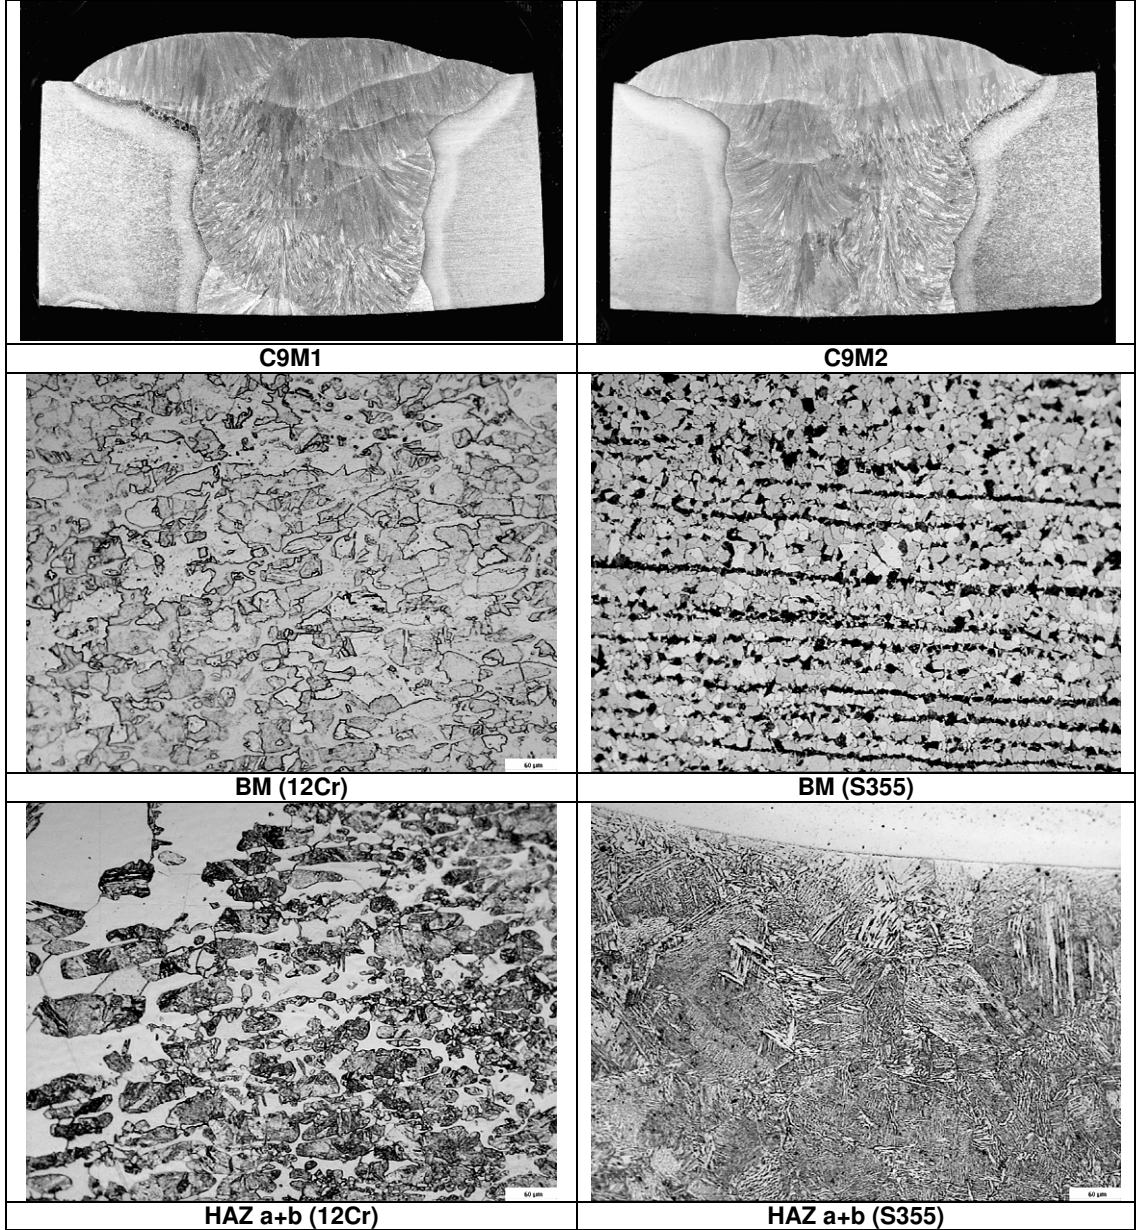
12 mm kalınlığında 309 tür ek metal ile farklı metal FCAW kaynaklı bağlantının makro ve mikroyapıları (U9).
